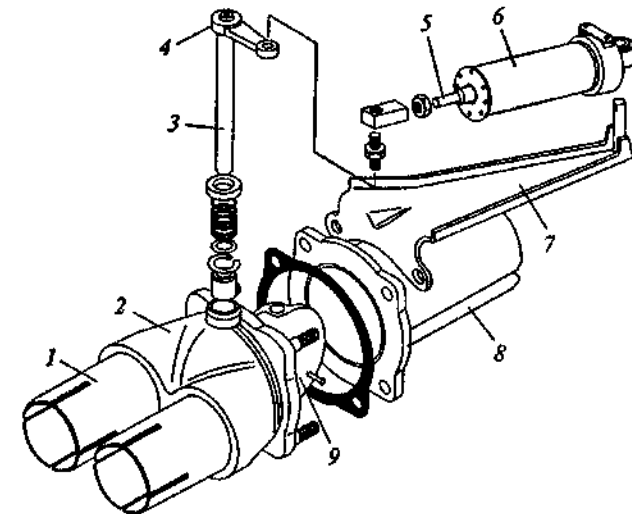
Моторный тормоз-замедлитель грузового автомобиля ЗИЛ:
